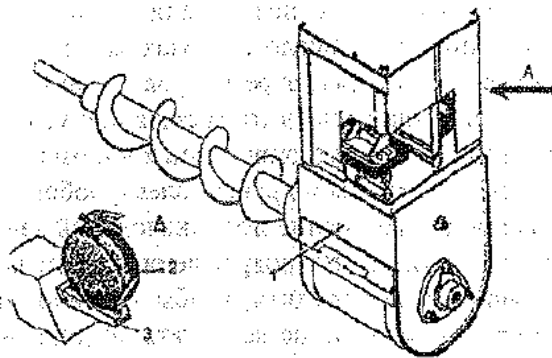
Огнетушитель на корпусе колосового элеватора: 1- корпус колосового элеватора; 2- огнетушитель; 3- кронштейн
